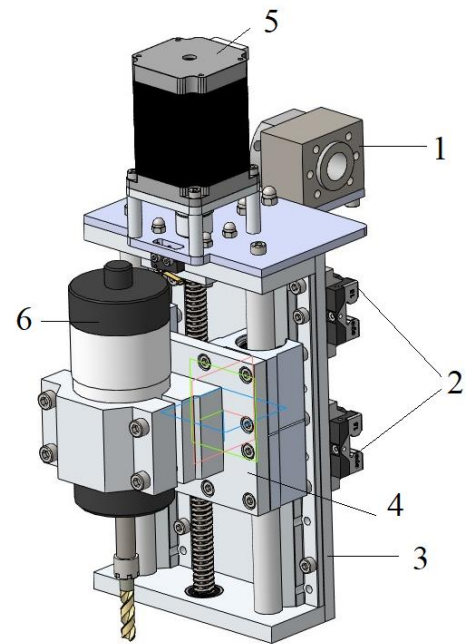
Общий вид крепления шпинделя фрезерного 3 – D станка.
